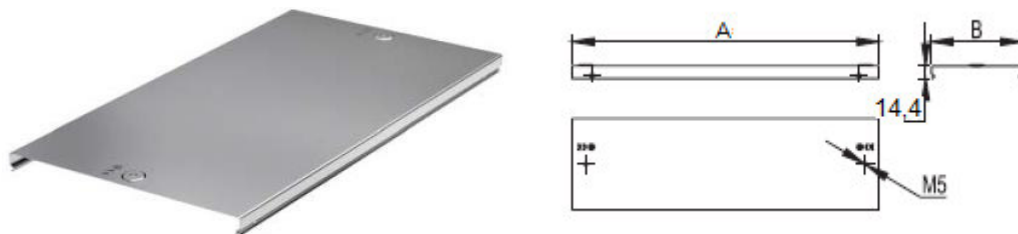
Крышка TDSR на ответвитель T-образный вертикальный переходник, типов: 3840, 3841
